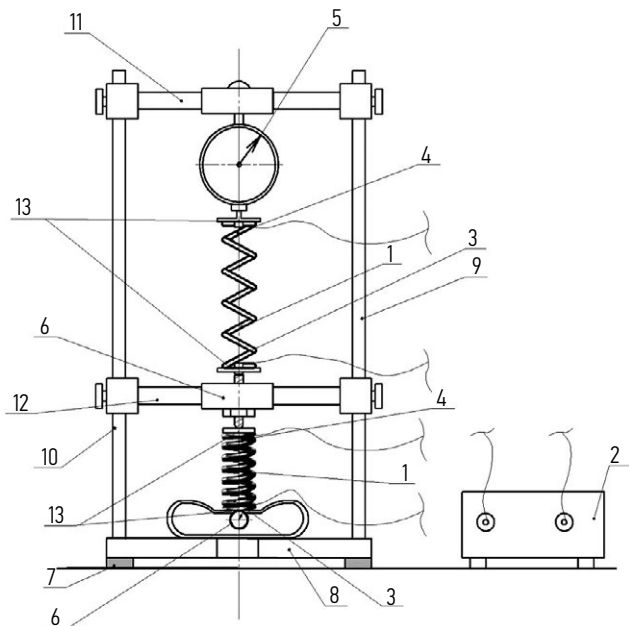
Схема устройства для неразрушающего контроля состояния винтовой цилиндрической пружины: 1 — цилиндрическая пружина; 2 — микроомметр; 3 и 4 — клеммы; 5 — динамометр на растяжение; 6 — динамометр на сжатие; 7 — рама; 8 — опорная плита; 9 и 10 — вертикальные стойки; 11 — верхний поперечный элемент; 12 — средний поперечный элемент; 13 — диэлектрические прокладки.
